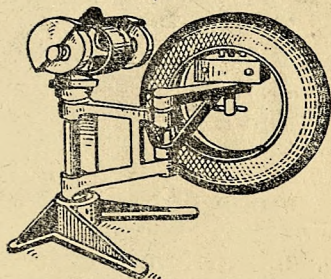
Современный шероховальный станок с приспособлением для поддержания покрышки
